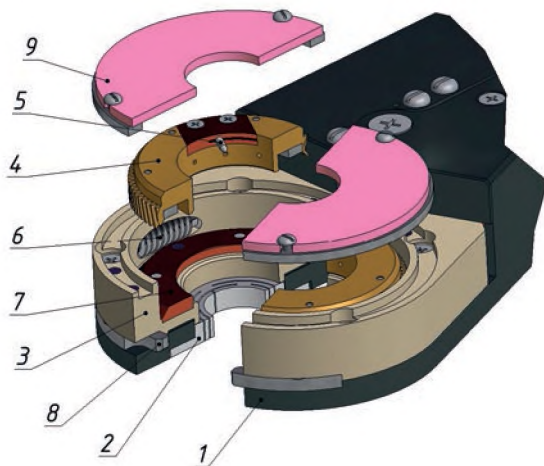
Конструкция разъёмной сварочной камеры
